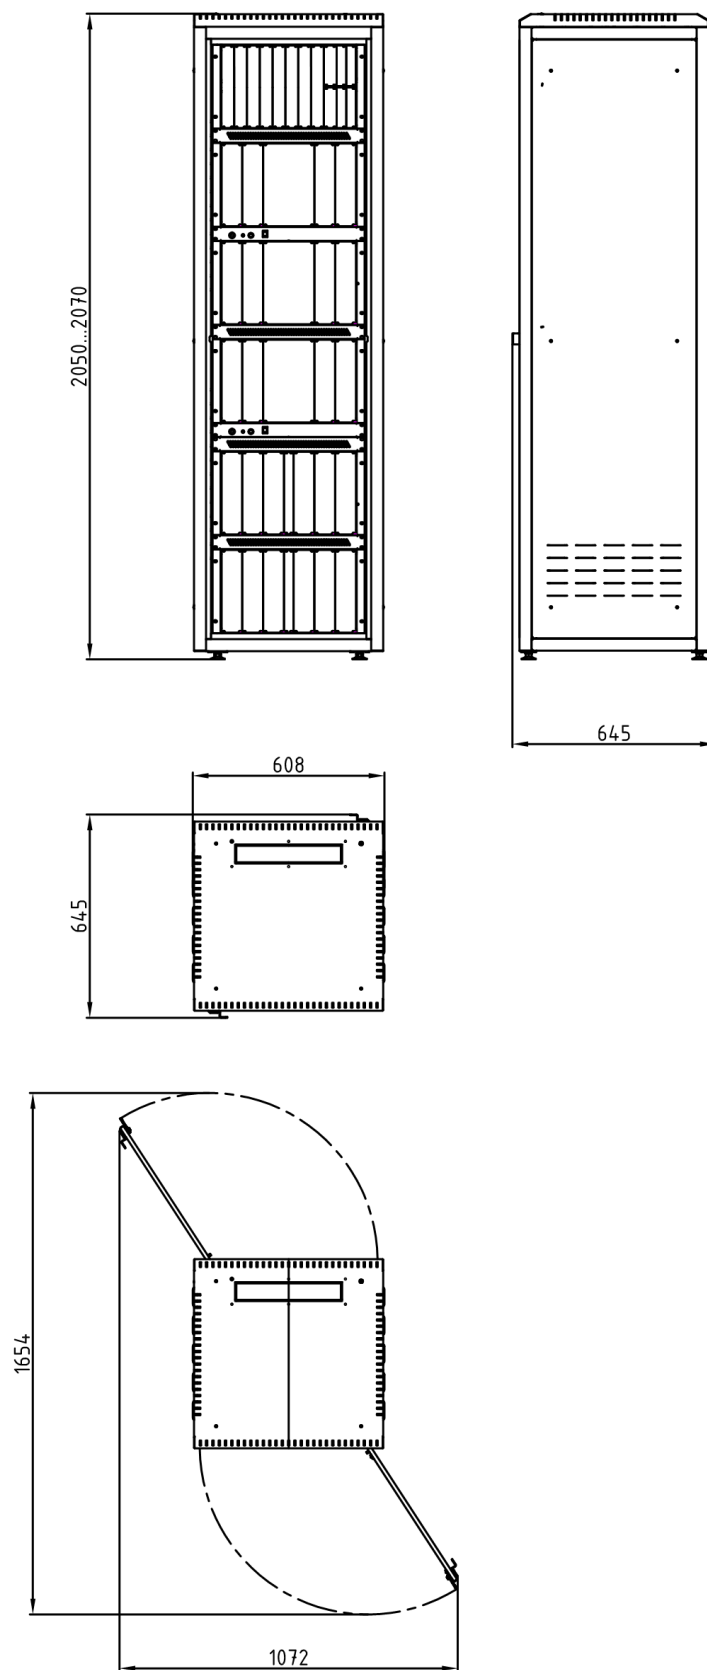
Габаритно-установочные размеры ЦМ КРЦ и ВЗУ-ЭЦС-Е
